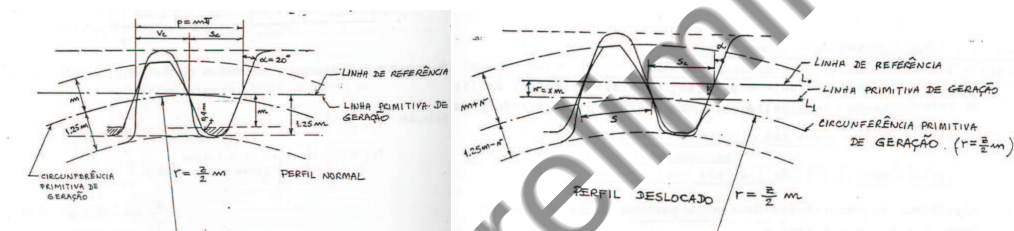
Afastamento da ferramenta na geração de engrenagens.
